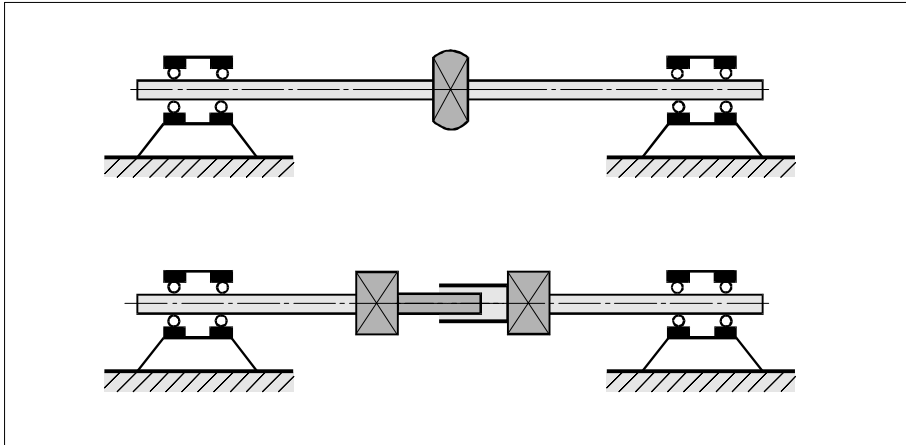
Axialversatz mit Ausgleichselement, oben Doppelgelenkkupplung, unten Gelenkwelle
